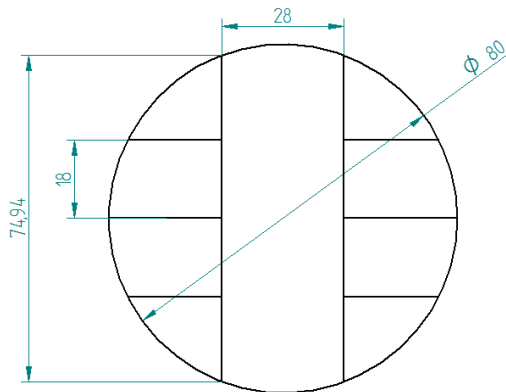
Esquema del diseño de corte de probetas. Fuente: Autor del proyecto
